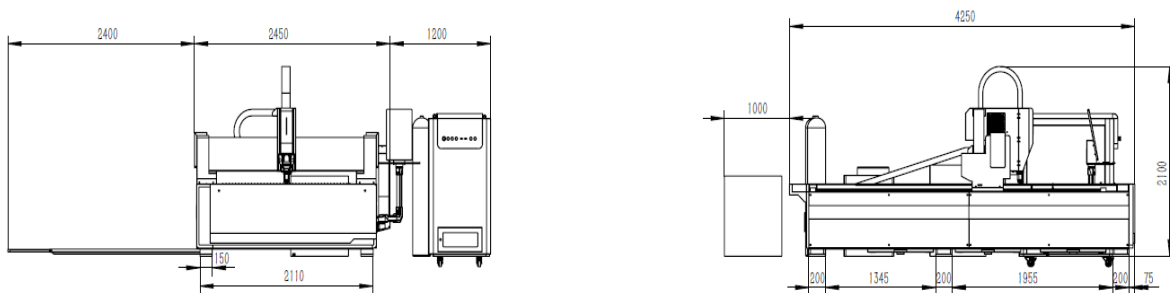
Габаритные размеры станка MetalTec 1530B (6000W)
